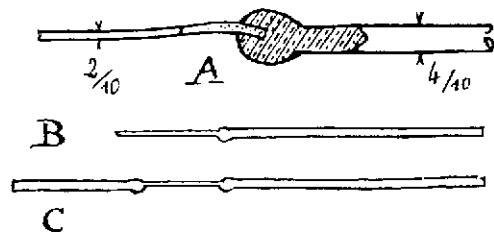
Détails de la soudure cuivre-platine.
